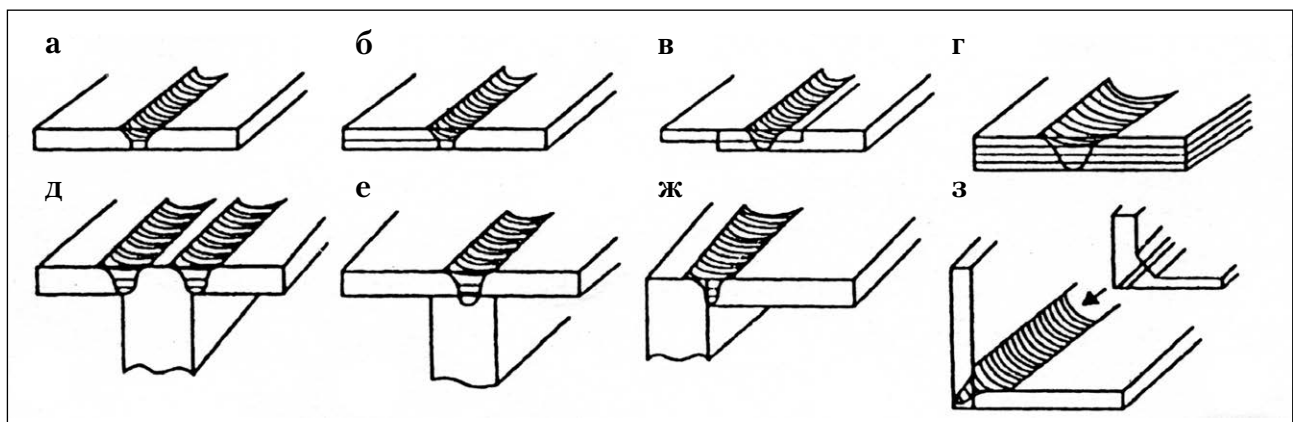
Типы выполняемых СТП соединений: а – стыковое; б – нахлесточно-стыковое; в – нахлесточное; г – многослойное нахлесточное; д – двухпроходное тавровое; е – тавровое прорезное; ж, з – угловое
